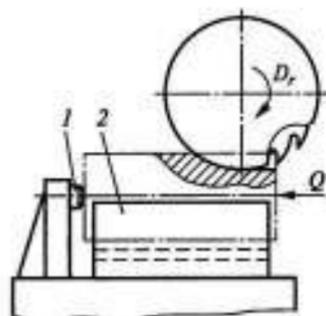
Установка и закрепление валика при фрезеровании:
